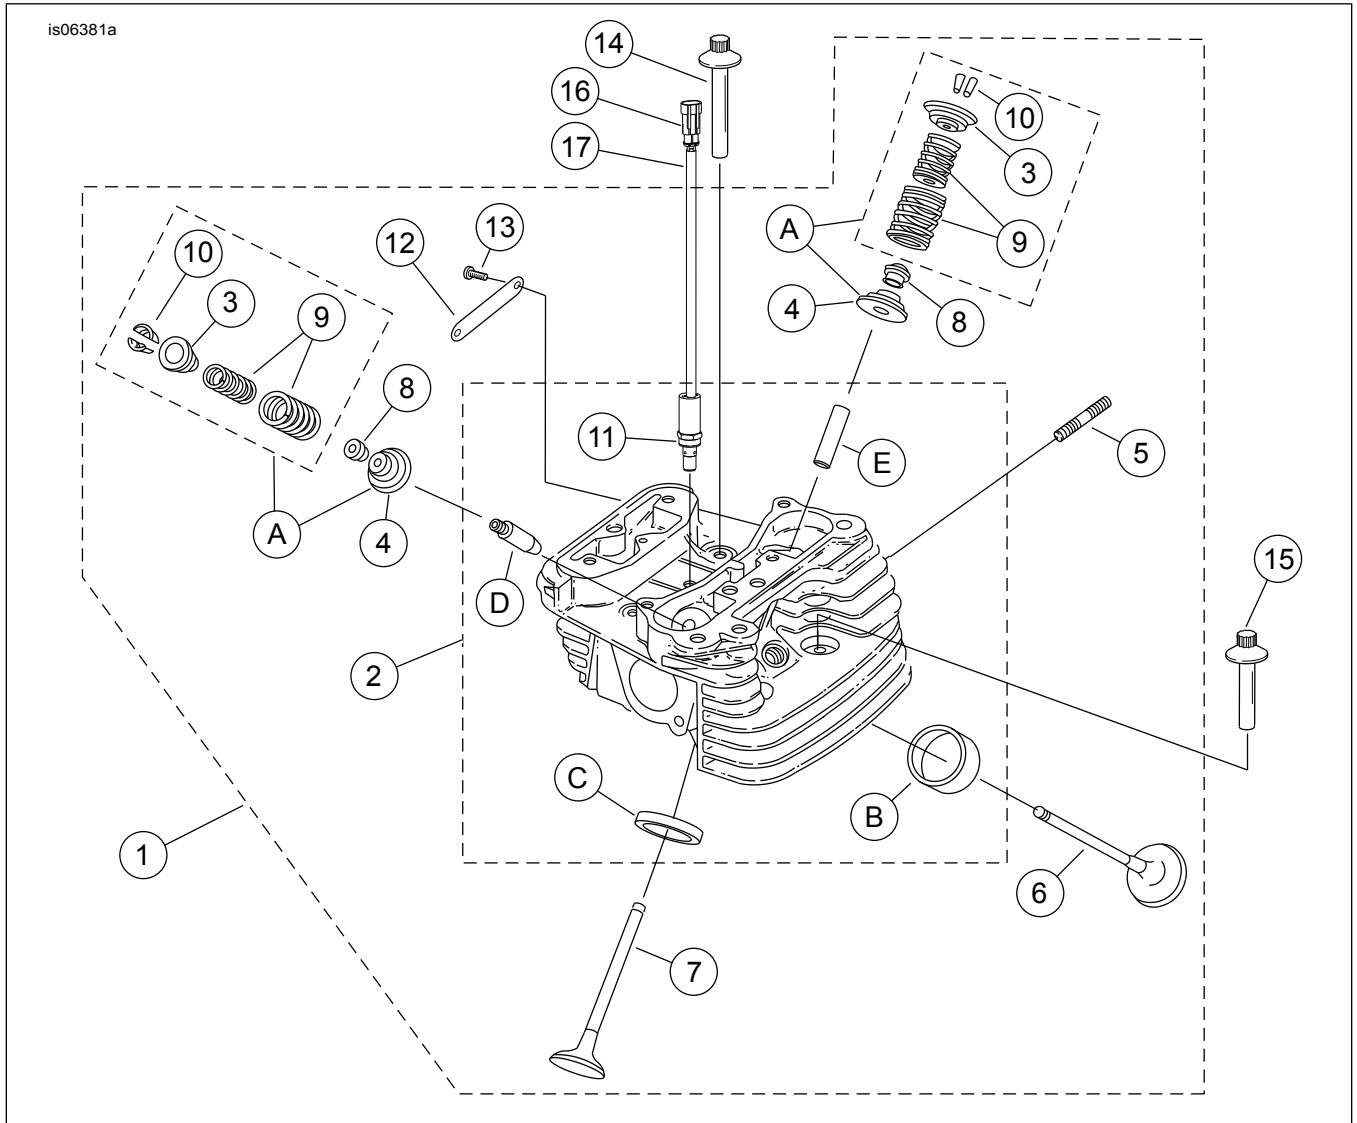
SE120ST Screamin' Eagle Crate Mga Cylinder Head at Valve ng Engine
